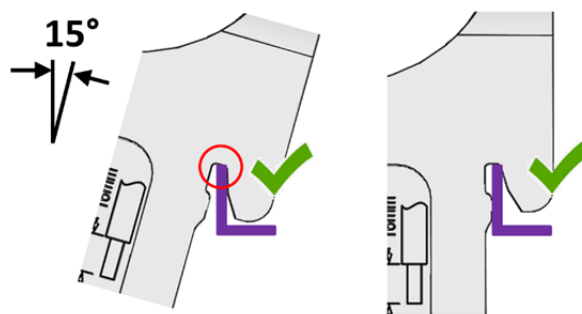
Prinzipdarstellung zum Einhängen (vor und nach dem Einrasten)
